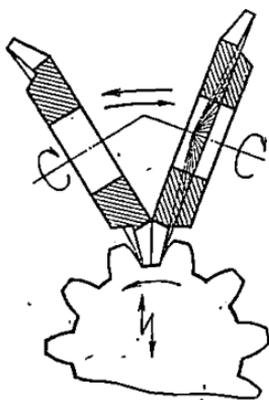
Обработка прямозубых конических колес по принципу обкатки двумя дисковыми фрезами.
